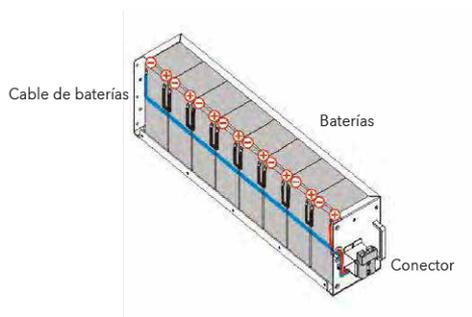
Instalación de baterías 3: instalación, cableado y fijación del conector de las baterías
